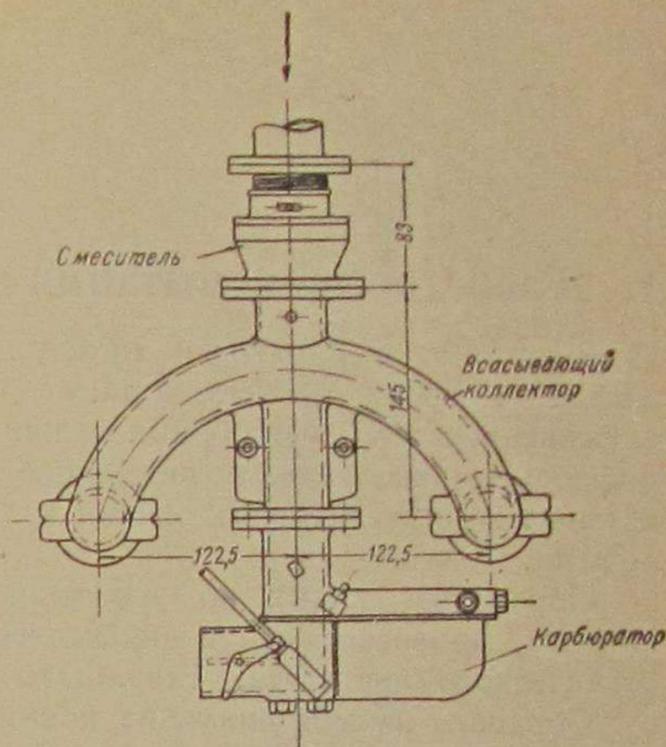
Установка газового смесителя У-5 и карбюратора на всасывающем трубопроводе двигателя.
